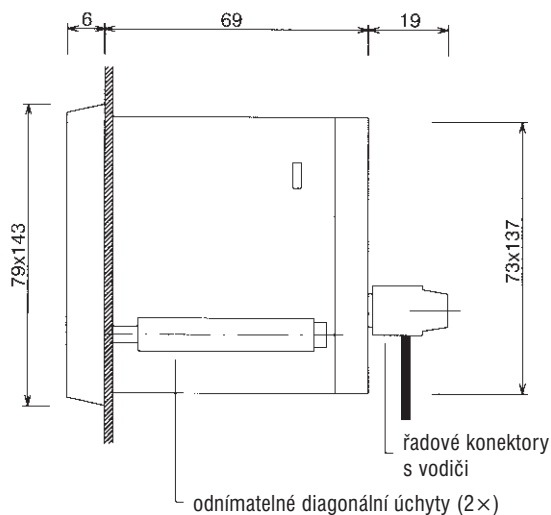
Rozměry snímacího proudového transformátoru SPT
